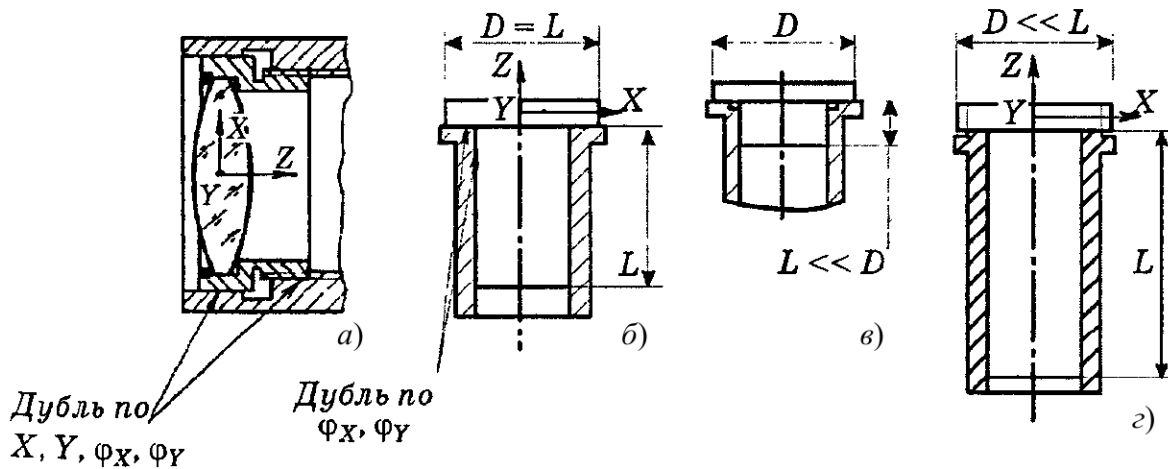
Спряження деталей в з'єднаннях за двома поверхнями
